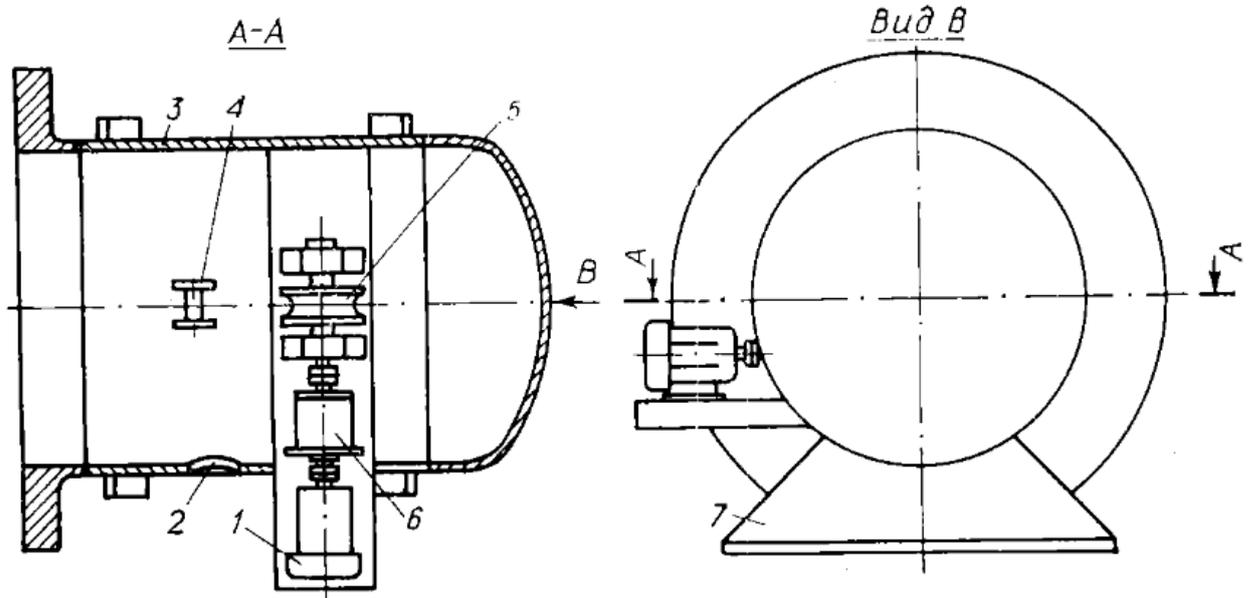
Переносное устройство: 1 – электродвигатель; 2 – окно; 3 – корпус; 4 – ролики; 5 – барабан; 6 – редуктор; 7 – опоры.
